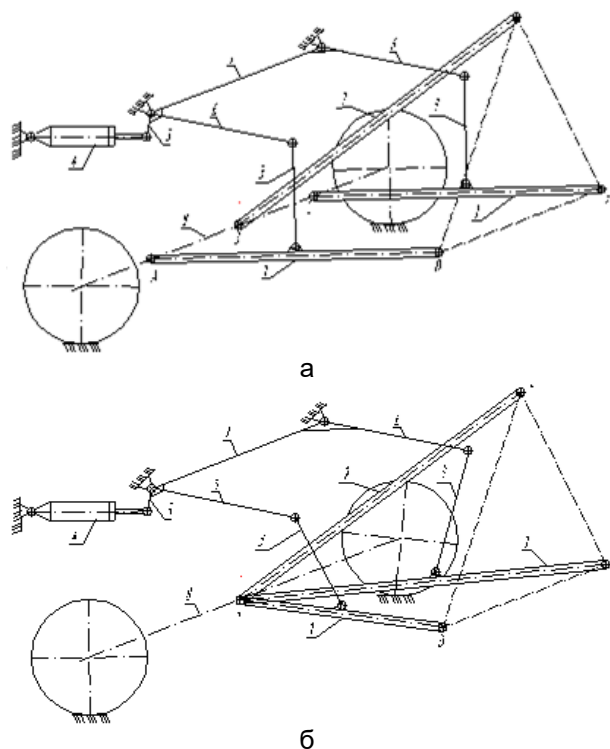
Схема удосконаленої начіпної системи колісного трактора для виконання ґрунтообробних робіт: а – схема для агрегатів з короткобазовими начіпними знаряддями; б – схема для агрегатів з довгобазовими начіпними знаряддями; 1 – нижні тяги начіпки; 2 – центральна тяга; 3 – розкоси; 4 – гідроциліндр; 5 – важіль штока гідроциліндра; 6 – важелі підйому знаряддя; 7 – верхня вісь начіпки; 8 – вісь симетрії задніх коліс трактора
